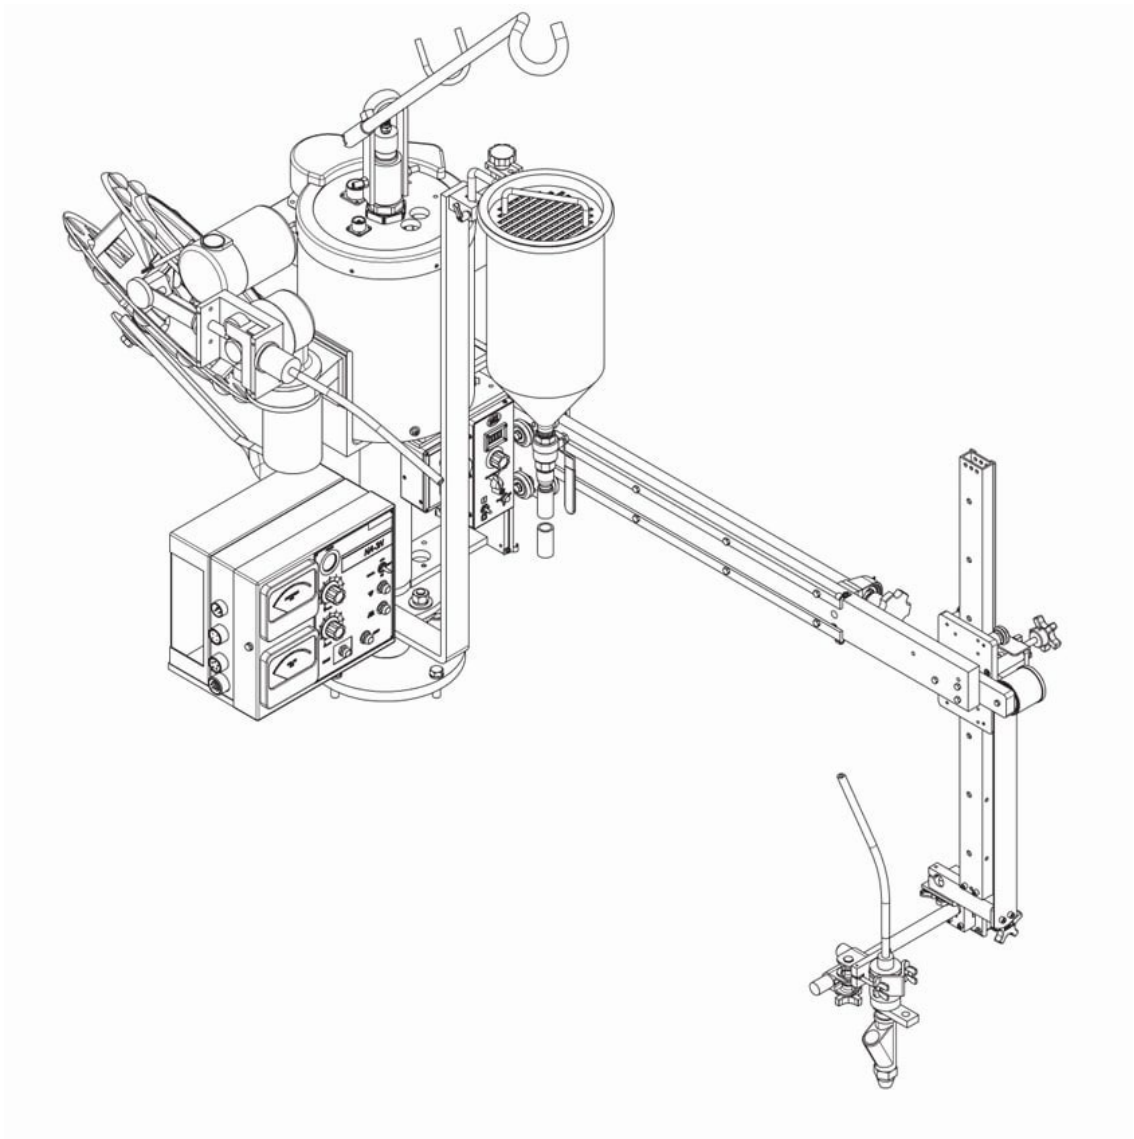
Зварювальний апарат CW–18 з круговим зварюванням
